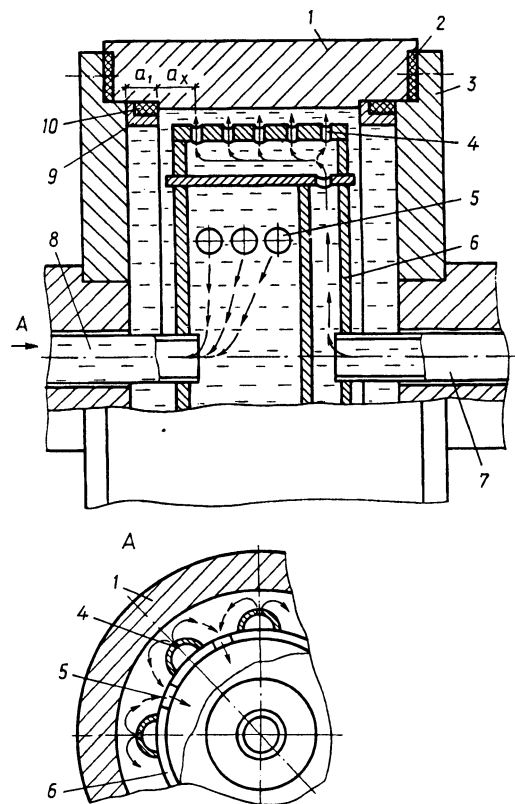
Схема системы охлаждения формообразующего валка с оптимизированными параметрами теплообмена на внутренней поверхности: 1 — корпус валка; 2 — прокладка; 3 — крышка; 4 — выпускные отверстия; 5 — водосборные отверстия; 6 — охладитель; 7, 8 — подводящие и отводящие трубы; 9 — обойма; 10 — теплоизолятор
